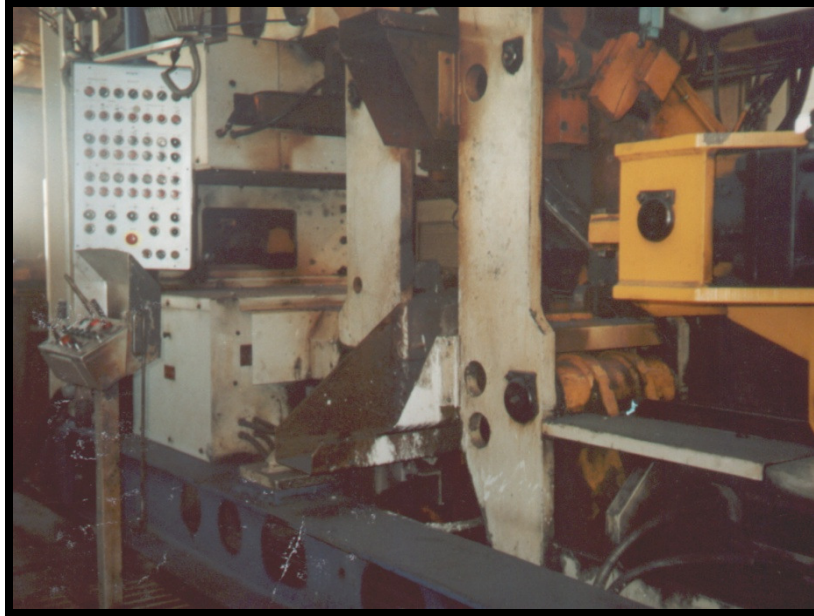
1 Mobil yakma alın kaynağı makinesi
